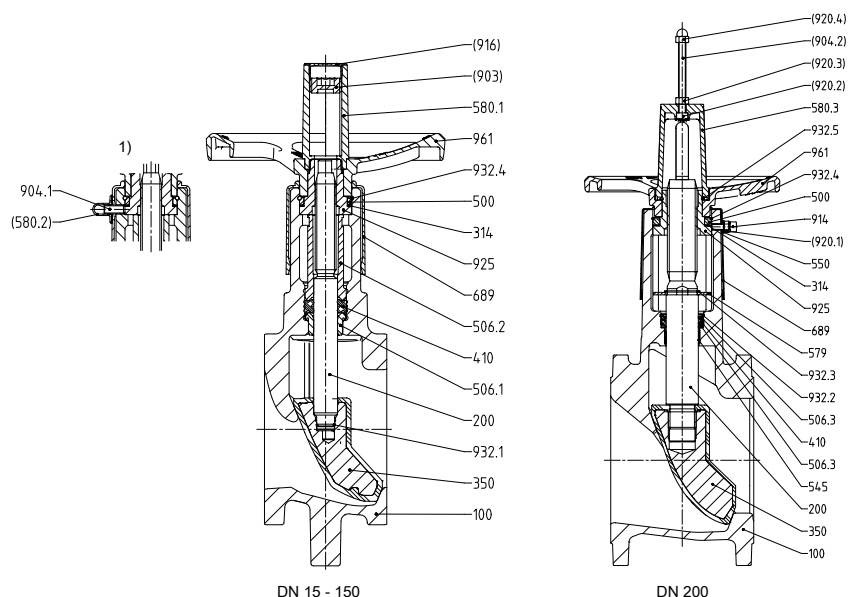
Disegni di sezione; 1) ruotati di 90°
